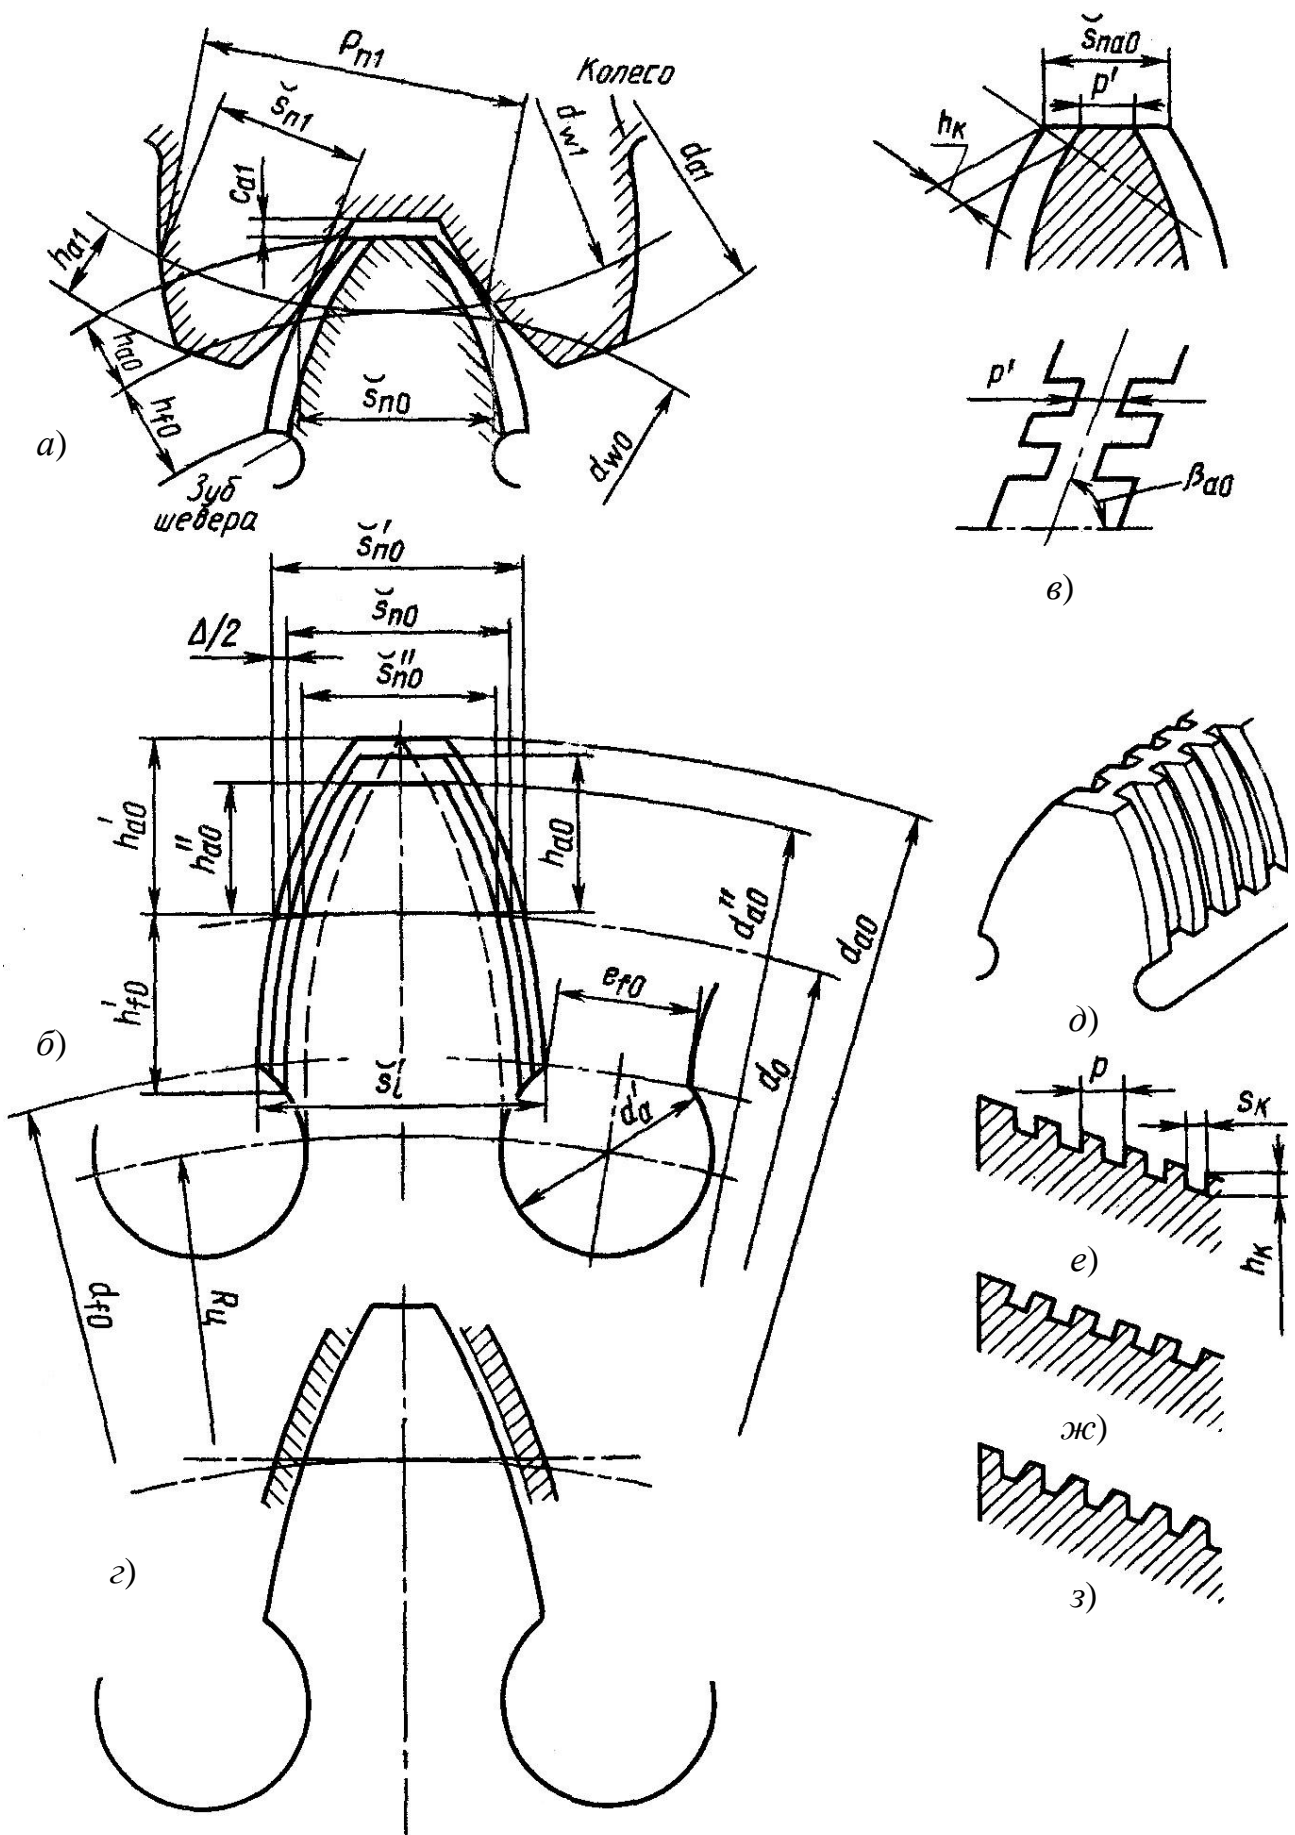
Размеры зуба шевера и стружечных канавок
